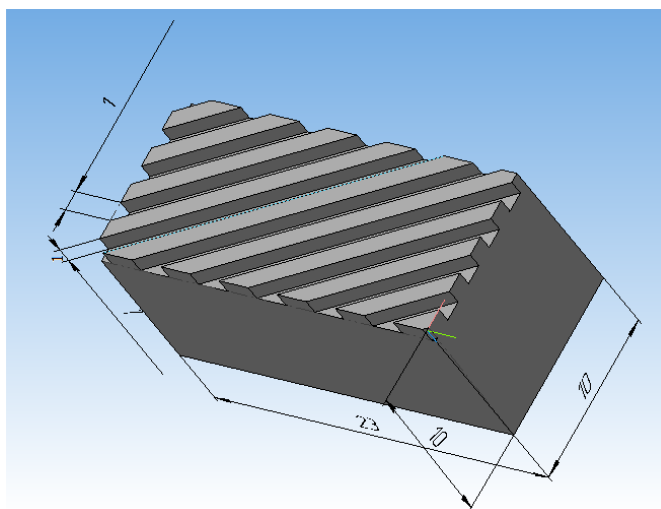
Эскиз фторопластовой подложки с пазами для металлической решетки
